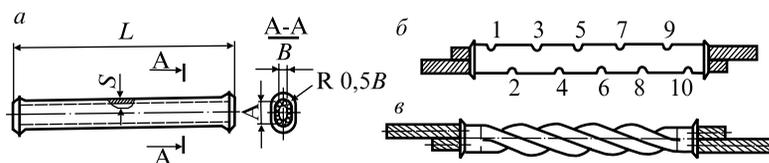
Овальный соединитель (а) и соединения проводов, выполненные обжатием (б) и скруткой (в) соединителя
